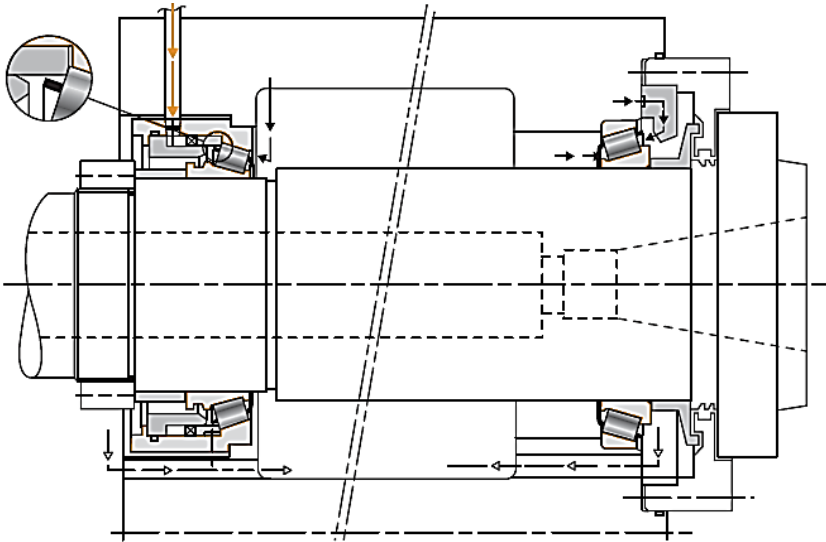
Шпиндельний вузол з конічними роликовими підшипниками в опорах
